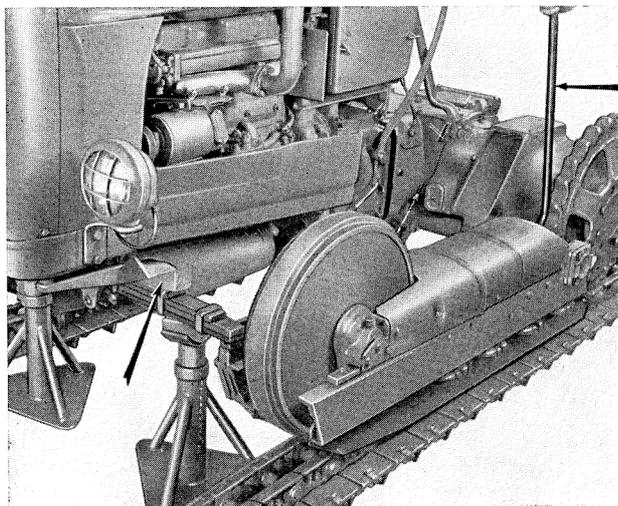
Séparation du moteur équipé de la boîte de vitesses et du carter de transmission arrière.
